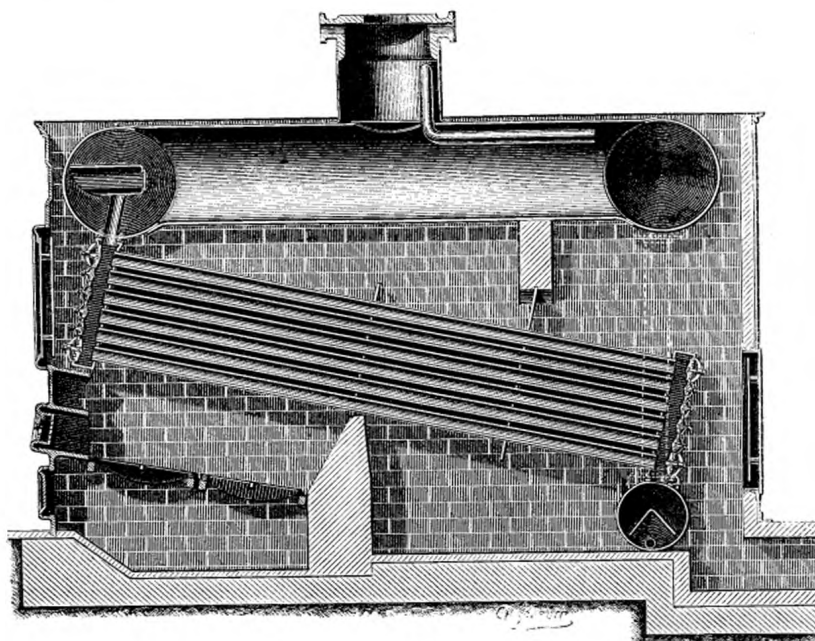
GÉNÉRATEUR, SYSTÈME MONTUPET. COUPE TRANSVERSALE
